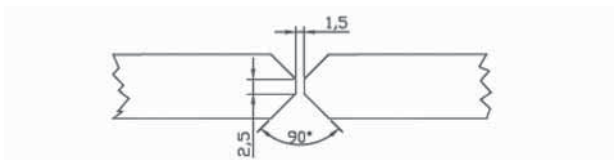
Preparación de bordes para soldadura de las placas.
